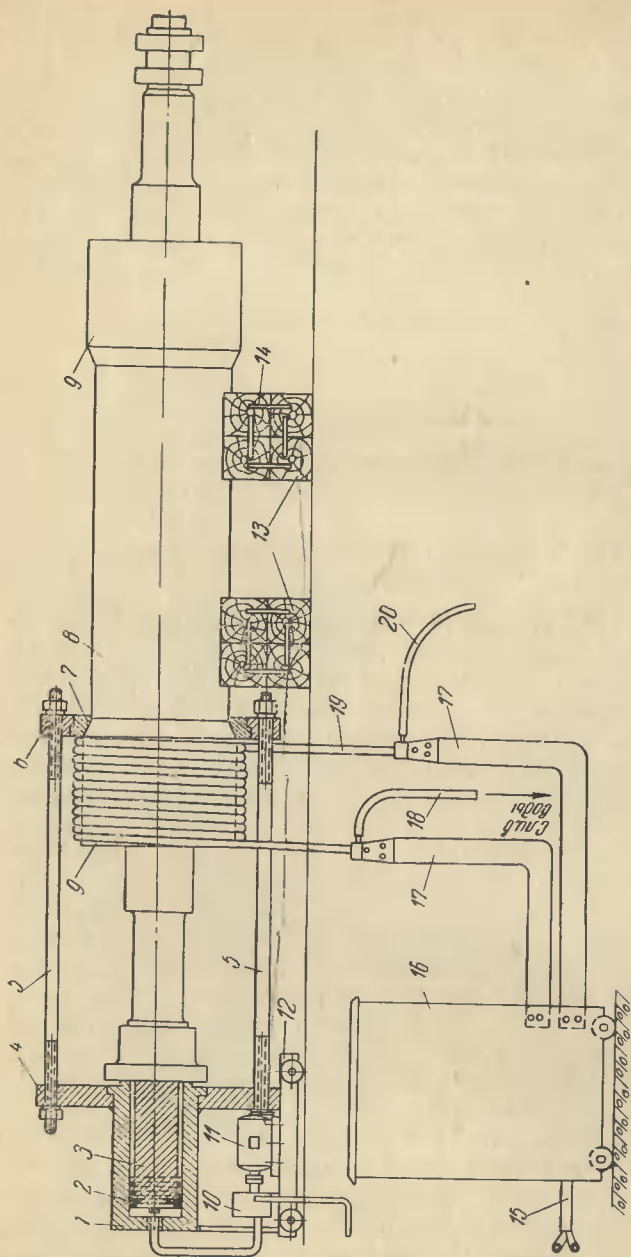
Установка ротора и приспособлений для съема бандажных колец индукционным нагревом.
